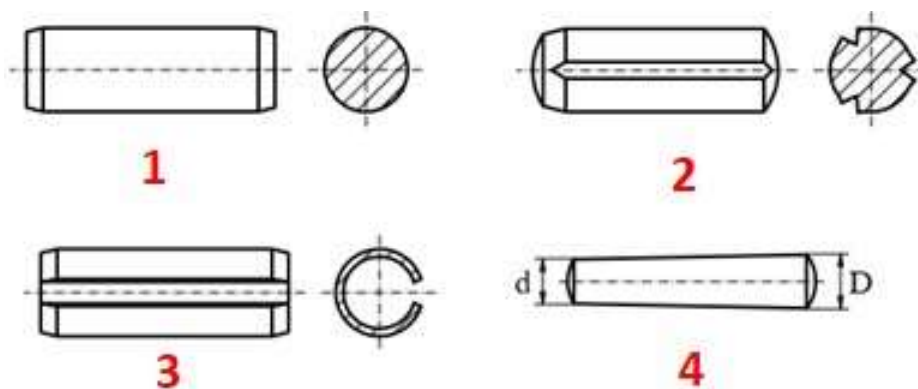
Виды штифтов: 1 – цилиндрический, 2 – зазубренный, 3 – сцепляющийся, 4 – конический
